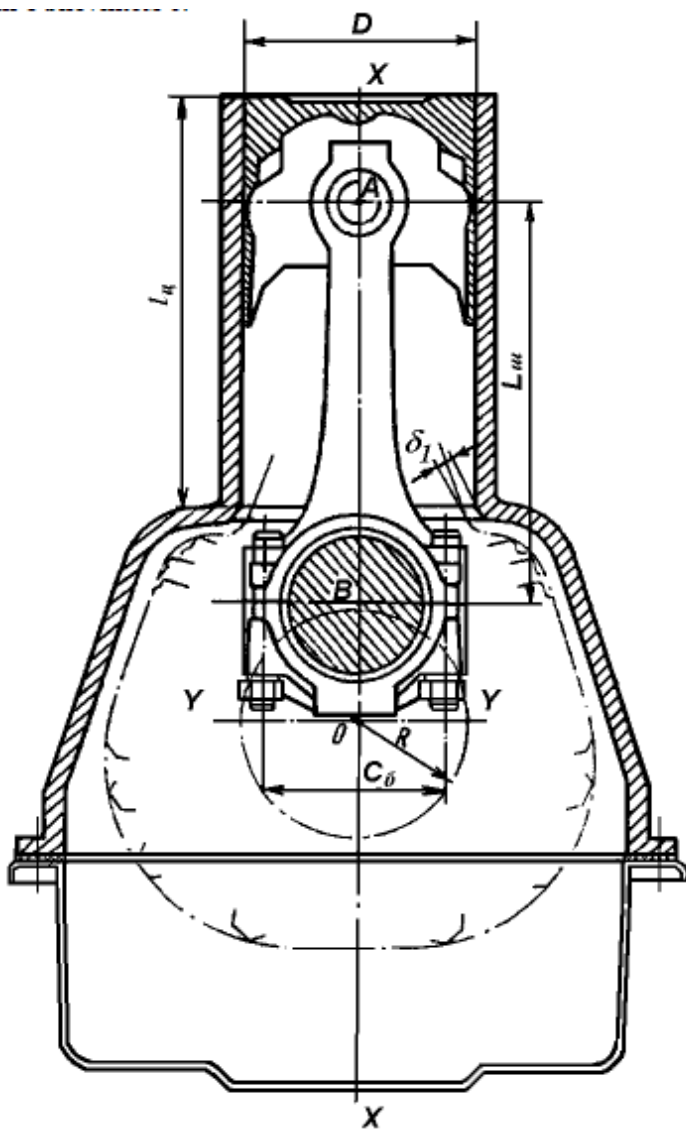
Компонировочная схема однорядного двигателя с вертикальным расположением цилиндров
